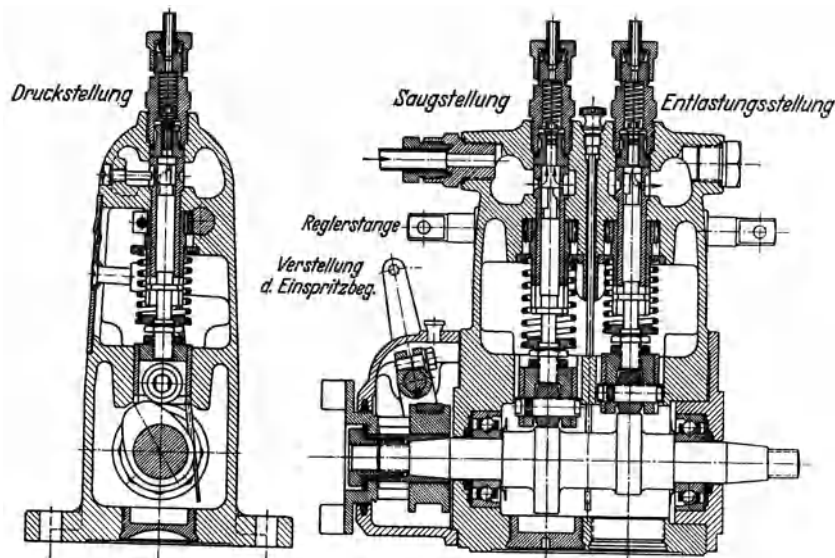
Einspritzpumpe für Dieseltreib der Rob. Bosch AG.
